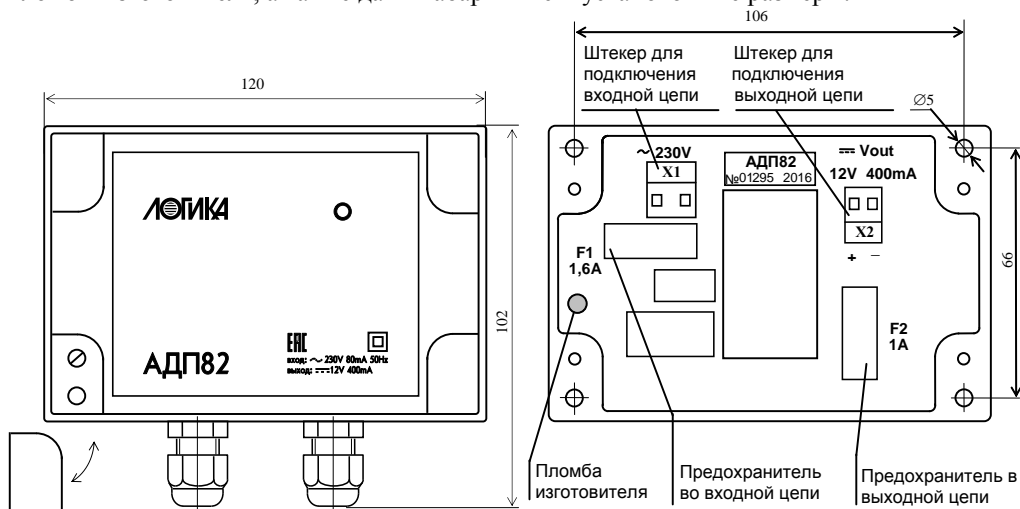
Общий вид адаптера и вид на монтажную панель
